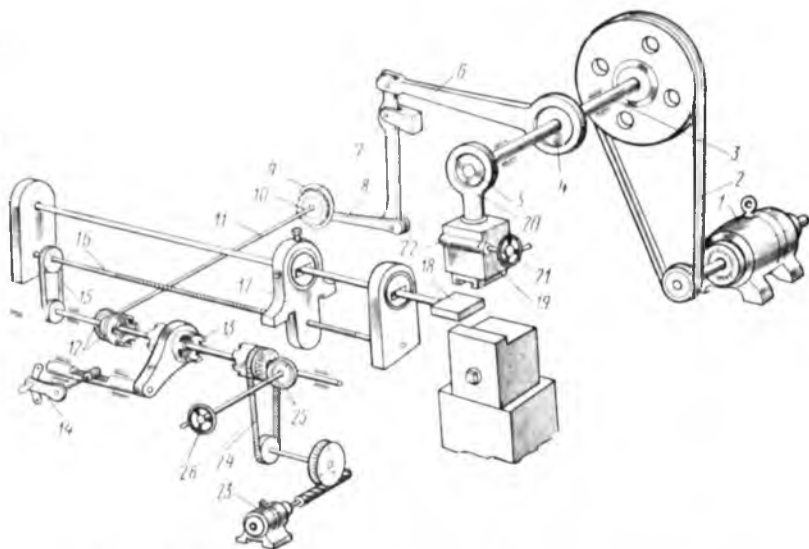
Кинематическая схема станка для гибки насечкой
